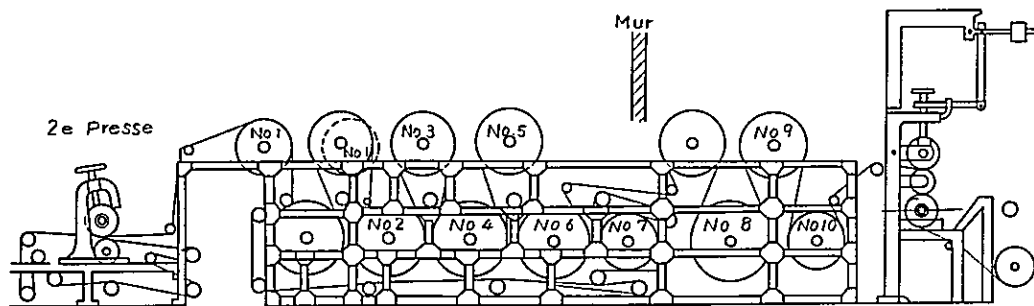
Machine à Papier à la P.C. d'Ain-El-Hadjar. Diagramme de Remontage
